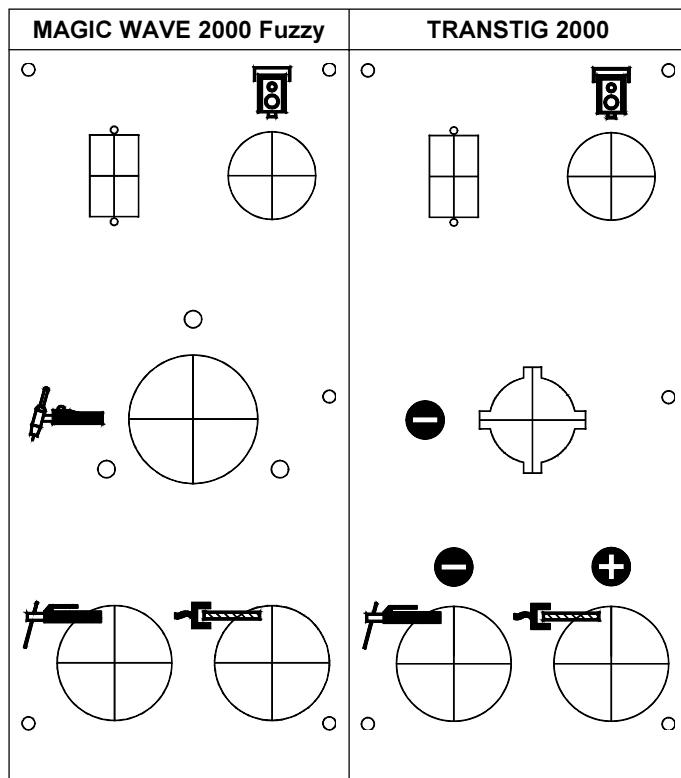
Torch et connexions du câble de soudage sur le front des appareils
